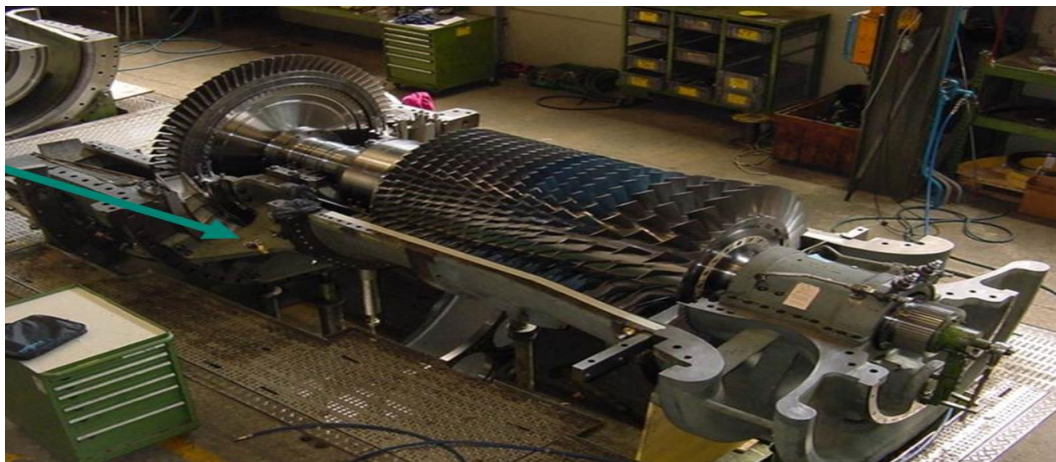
Ensemble corps (stator) du Compresseur et rotor de Turbine H.P [11]
